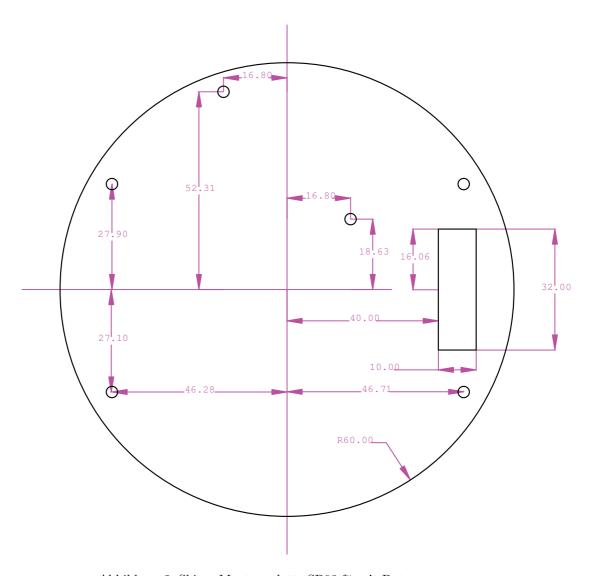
Skizze Montageplatte SP03 für c't-Bot
